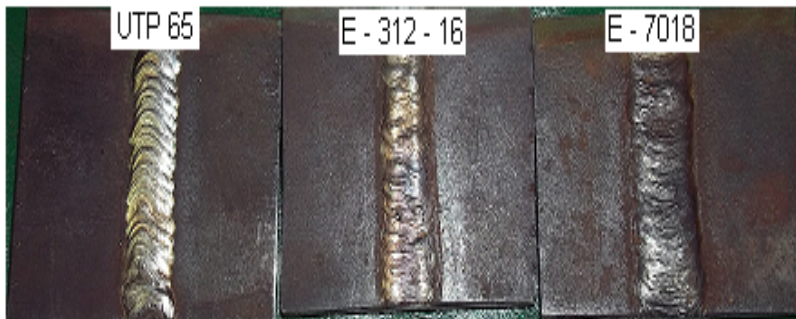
Electrodo empleados en la soldadura.
